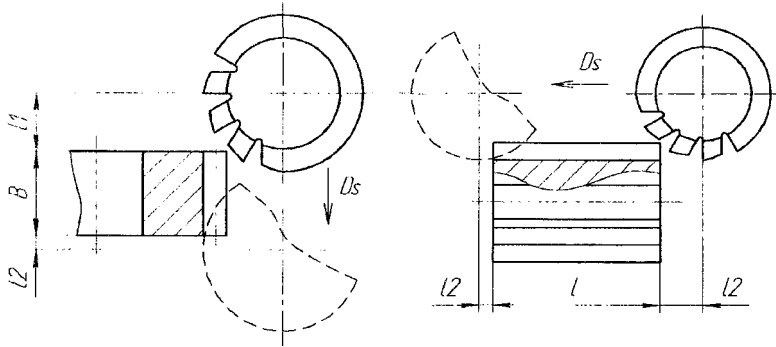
Зубофрезерование зубчатых колес и фрезерование шлицев червячными фрезами
